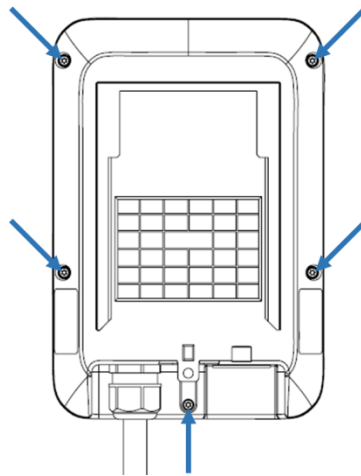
Emplacement des 5 vis Torx pour enlever le boîtier de la borne de recharge
